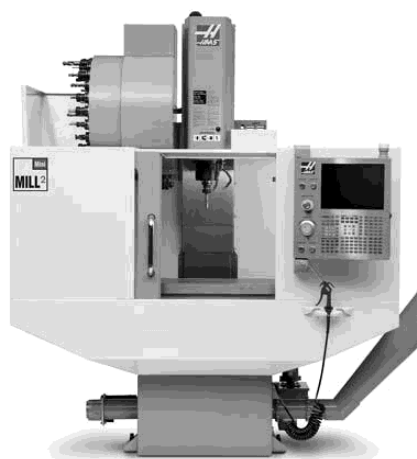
Вертикальный обрабатывающий центр Mini Mill 2
